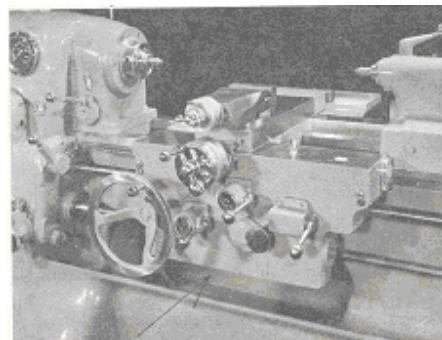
Delantal del torno (Cortesía de The Monarca Machina Tool Company, Sydney, Ohio).
